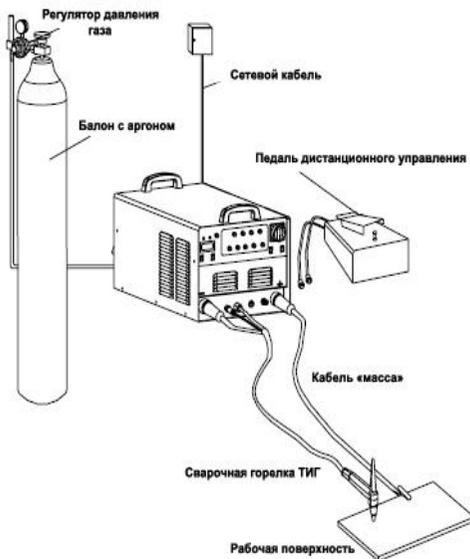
Схема подключения установки для аргодуговой сварки
